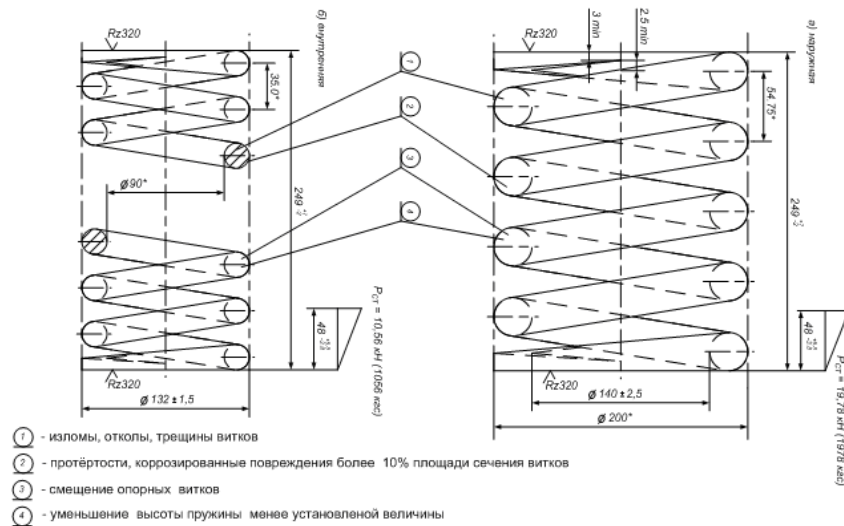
Пружины с указанными дефектами подлежат браковке.
